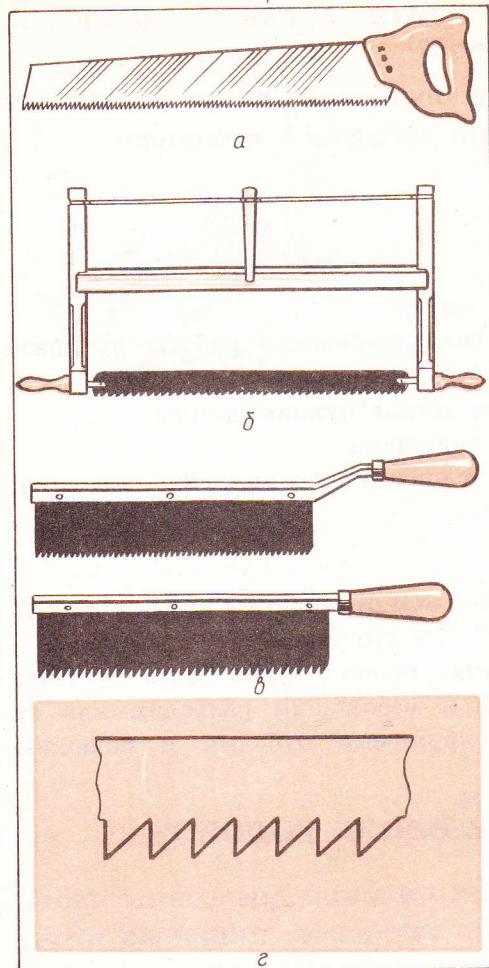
Пилы для пиления древесины вдоль волокон: а — ножовка; б — лучковая; в — шиповая; г — форма зубьев продольной пилы.
